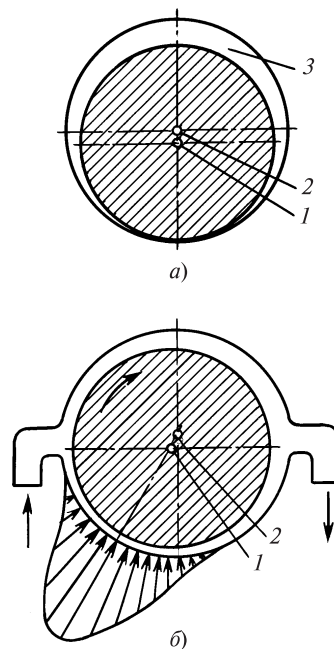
Схемы, поясняющие работу опорного подшипника
